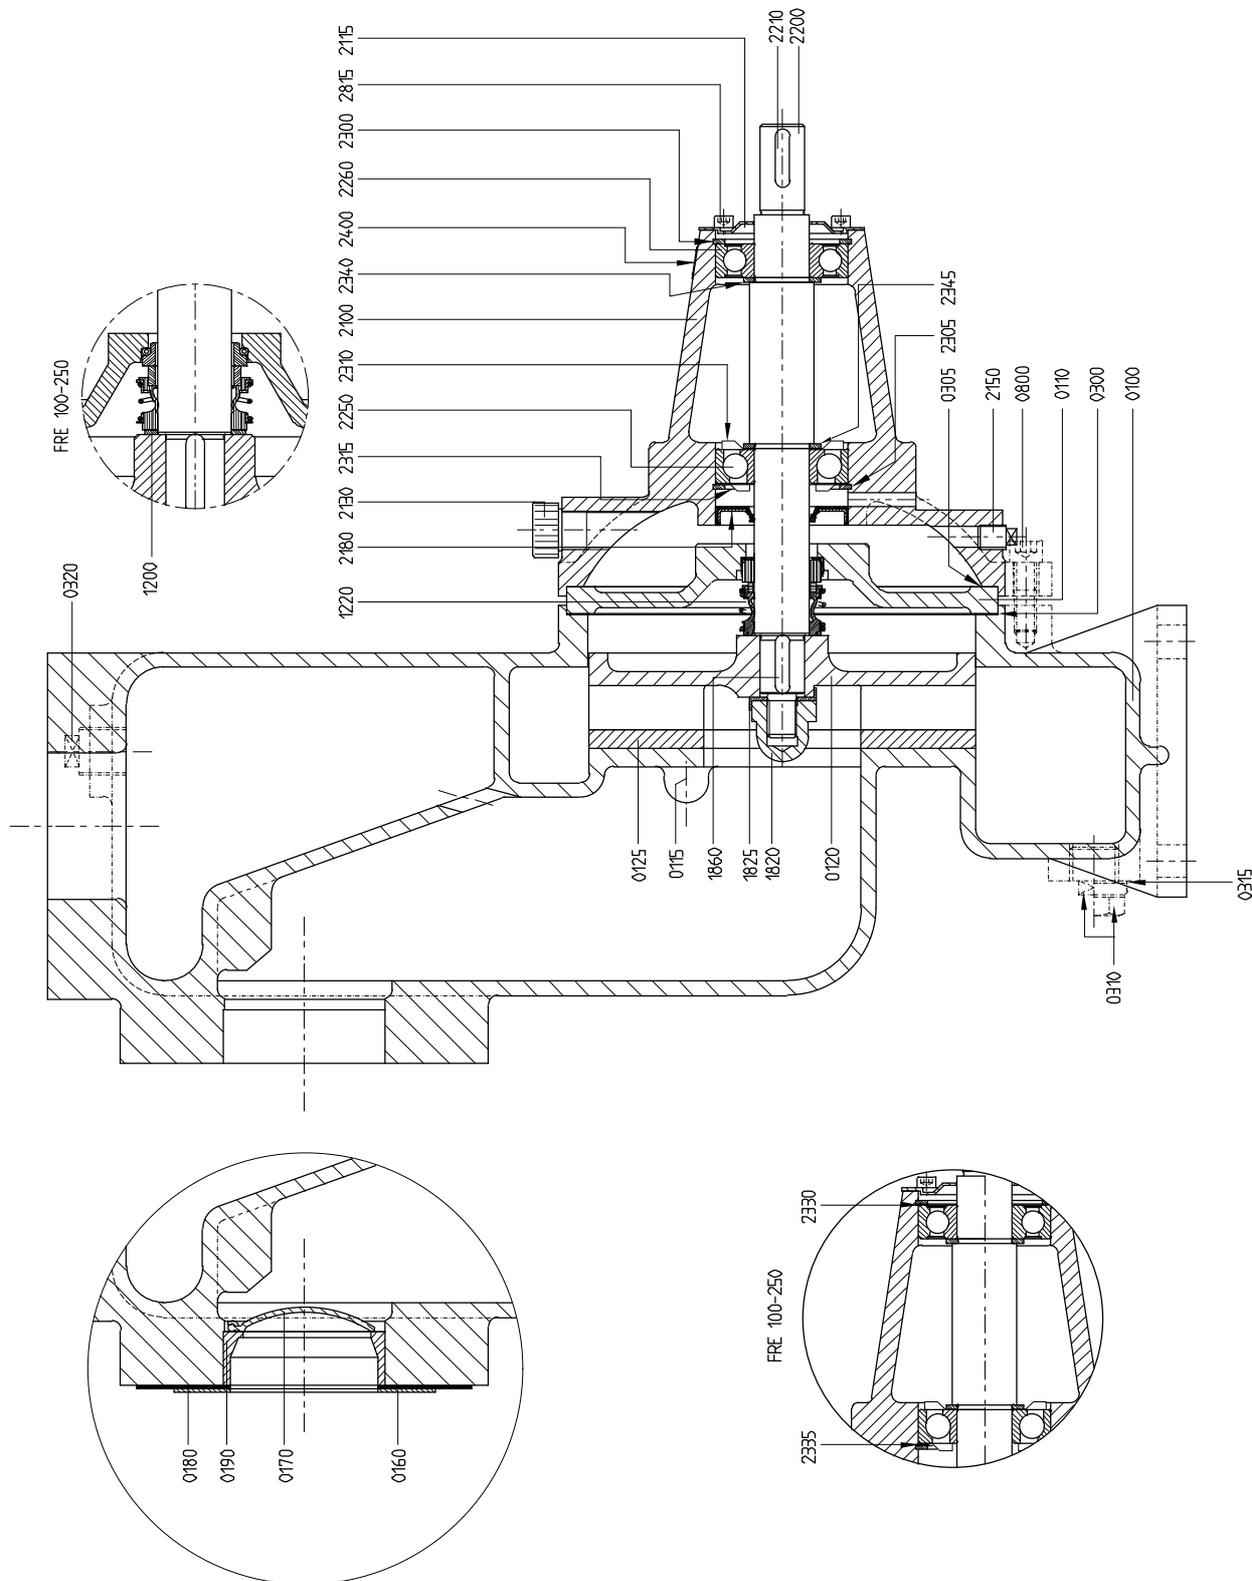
Plan en coupe FRE 80-210 et 100-250.
